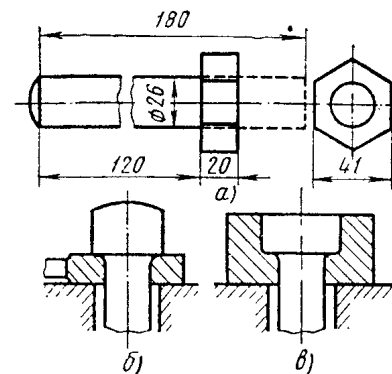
Схема фасоннойковки с применением подкладного штампа: а — эскиз поковки болта, б — оформление перехода головки к стержню, в — формовка головки болта
